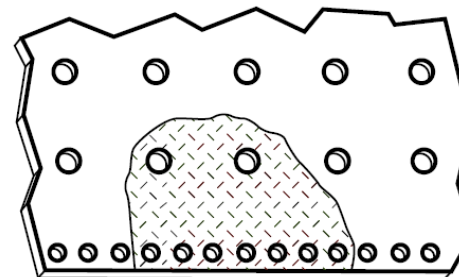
aRECONSTRUCCIÓN POR SOLDADURA DE AREAS
